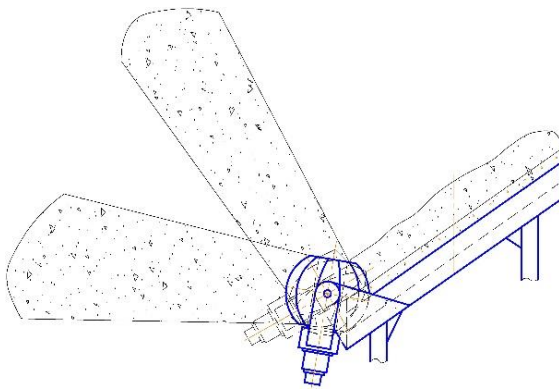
Косовстановлений відвальний робочий орган із циліндричним лопатевим металником для бічного транспортування ґрунту
